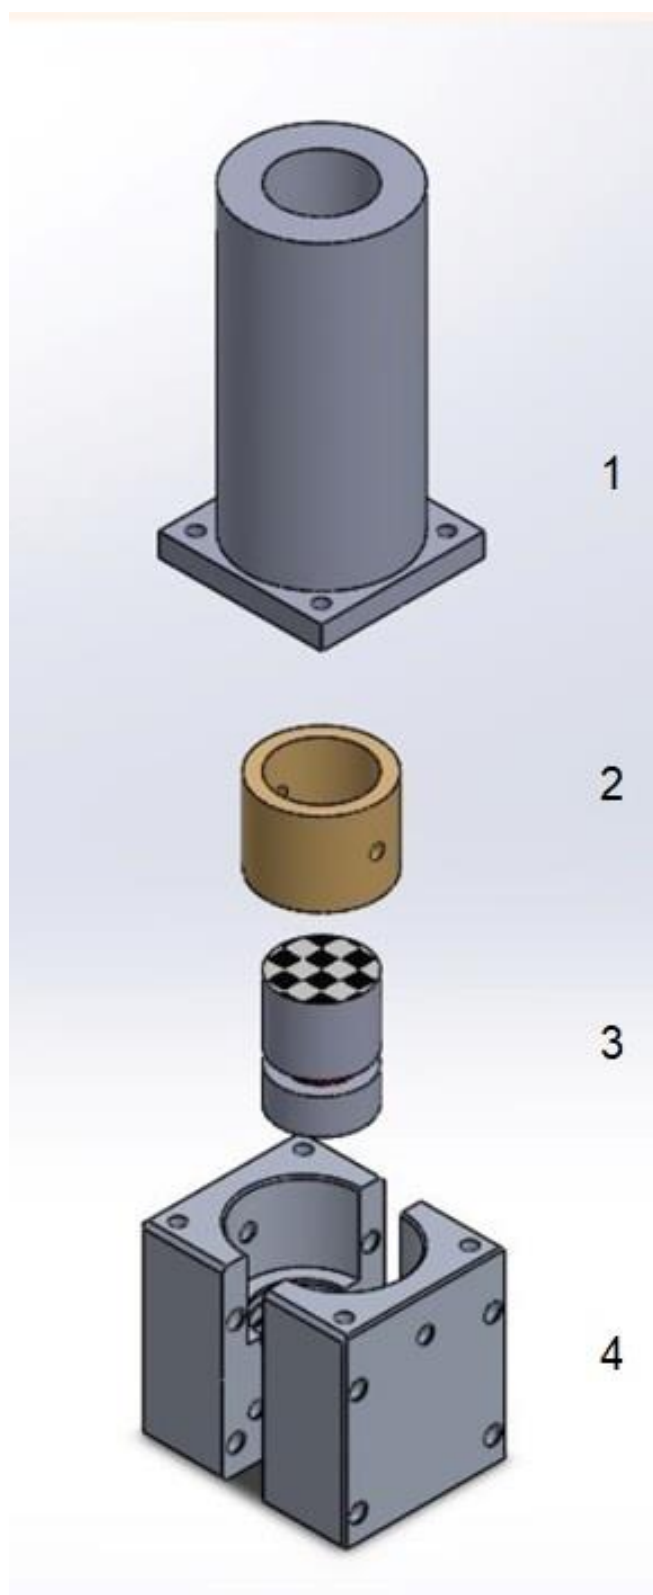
Vis ta explodida do molde em perspectiva isométrica
